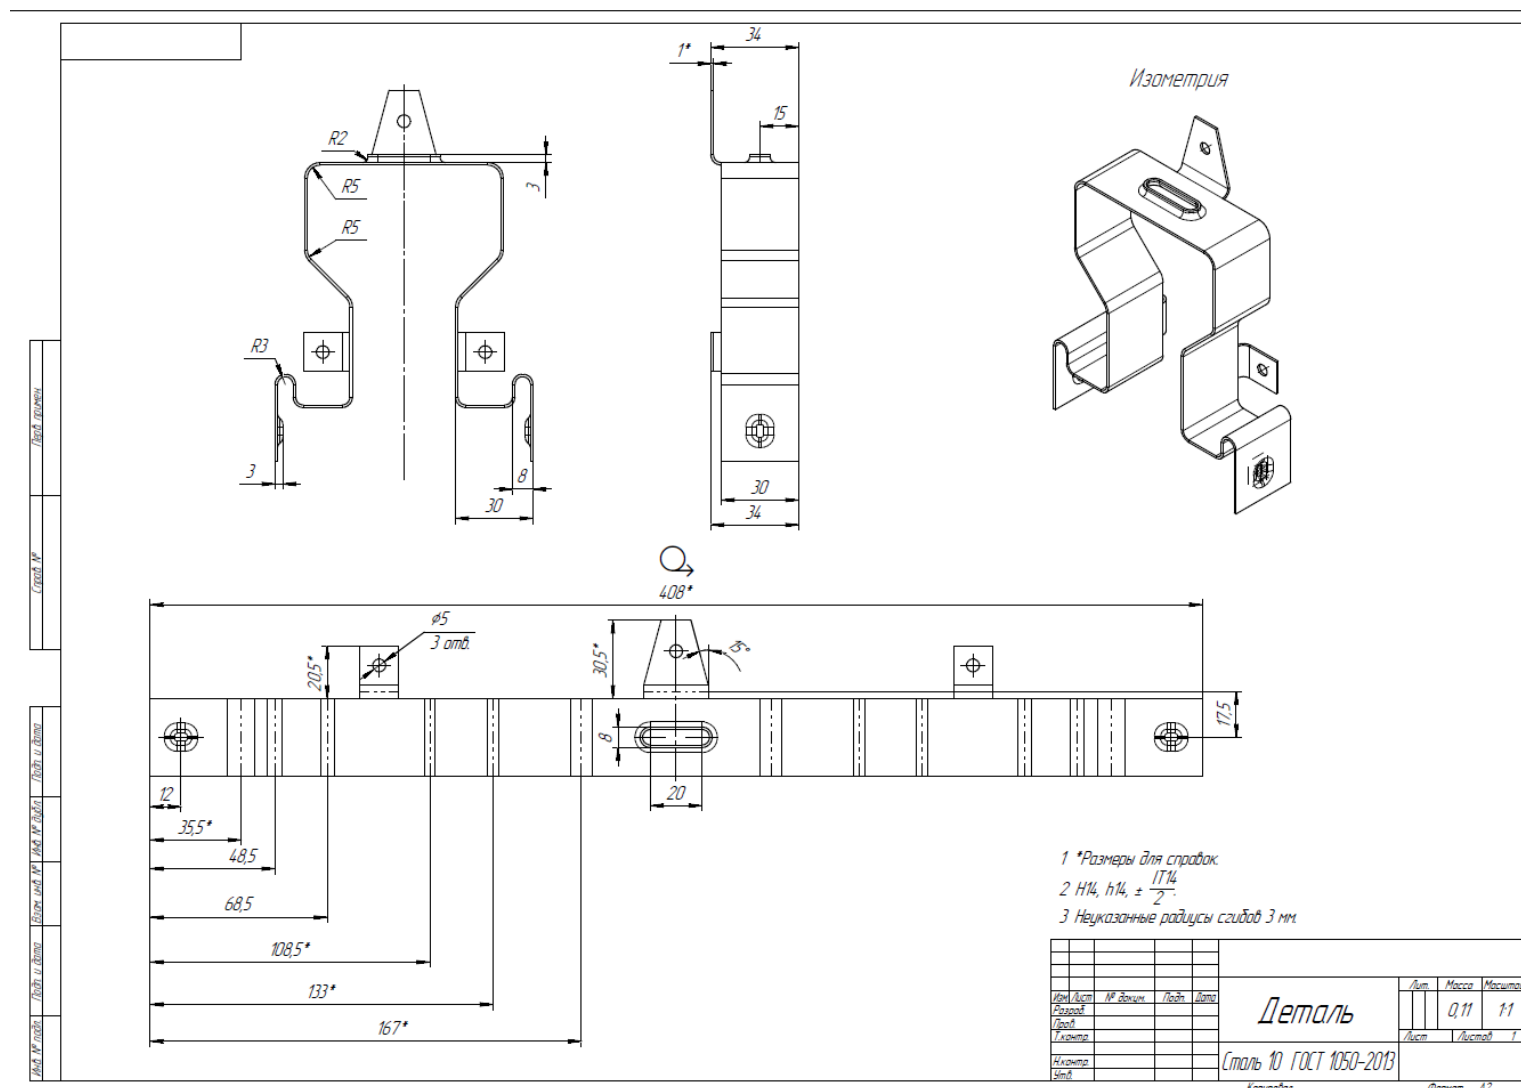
Чертеж детали «Кронштейн» (вариант 5)
